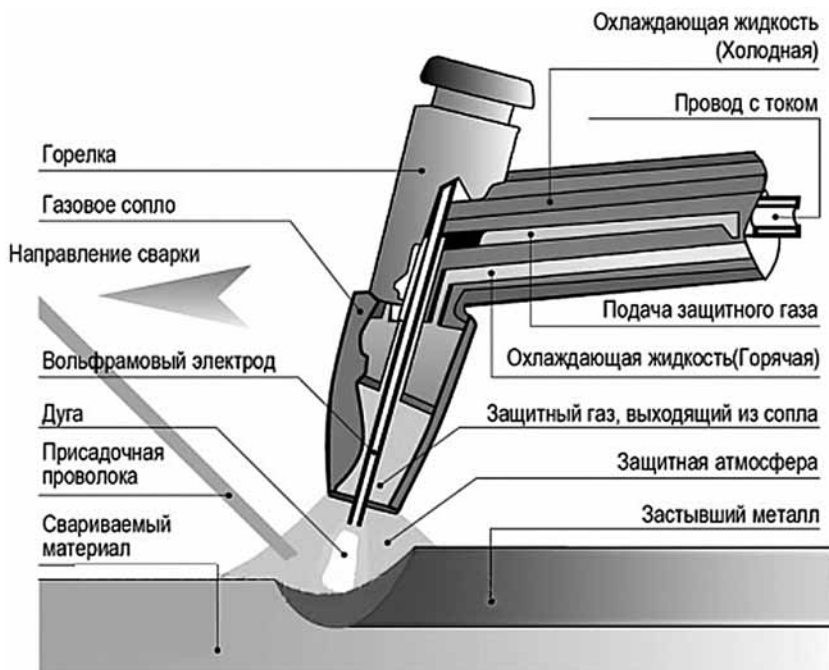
Схема сварки в защитных газах неплавящимся электродом.
